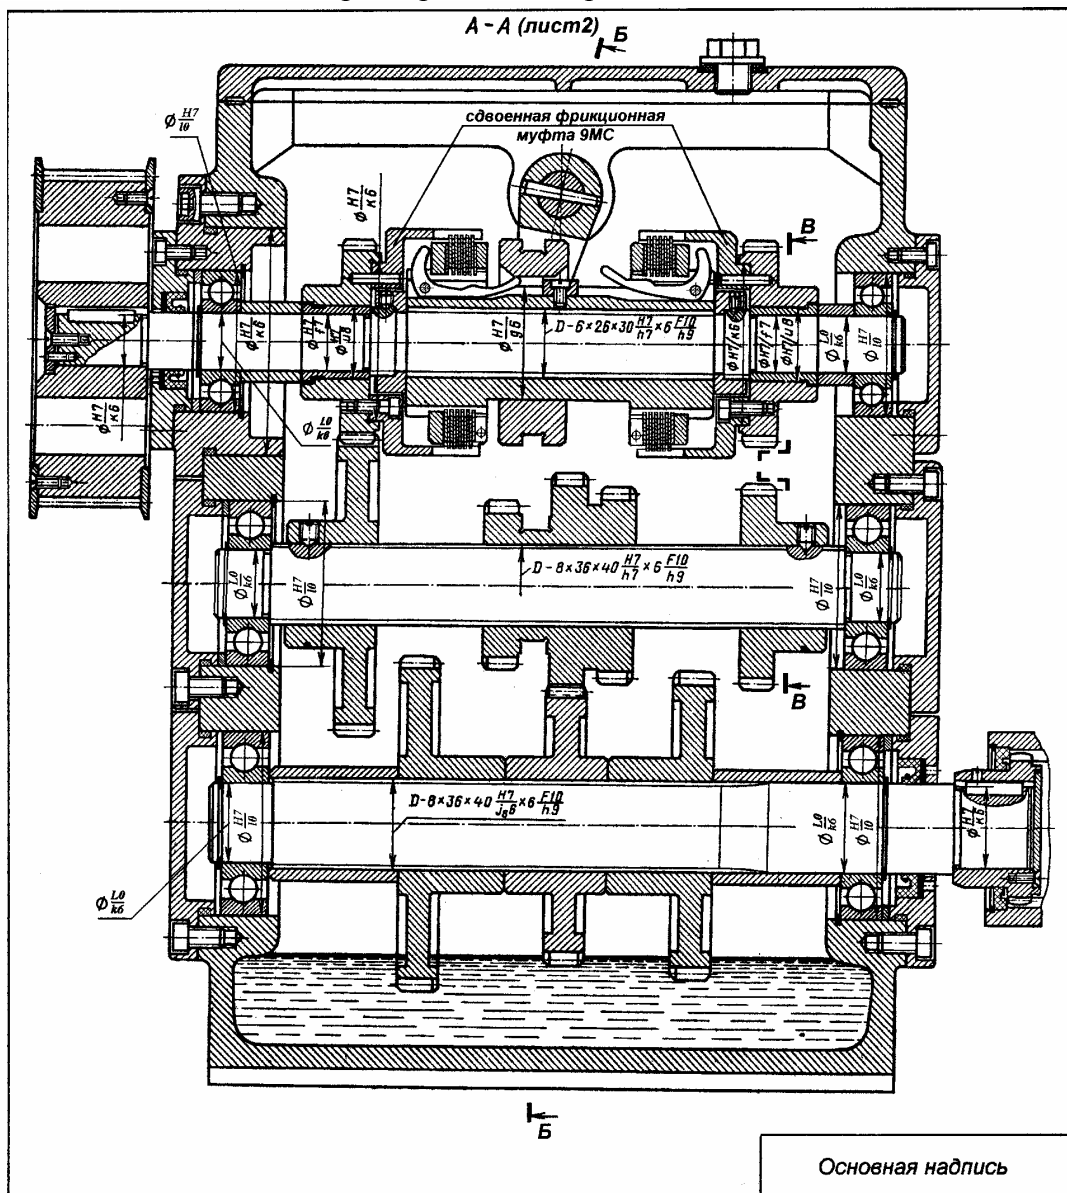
Шестискоростная коробка скоростей (развертка – лист 1)
